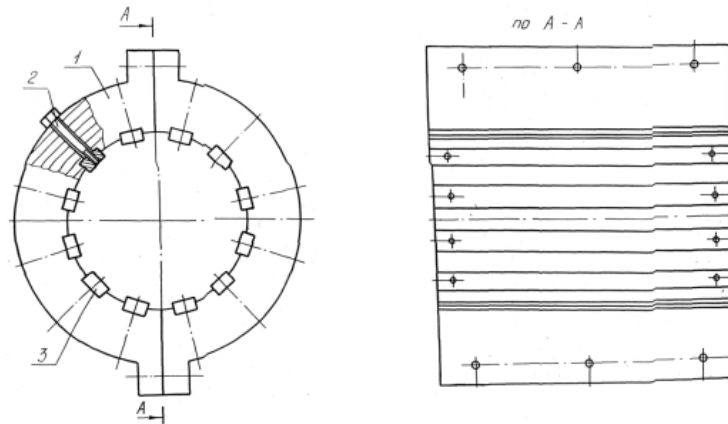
Корпус циліндра 1 - півкорпуси; 2 - гвинт; 3 - планка.
